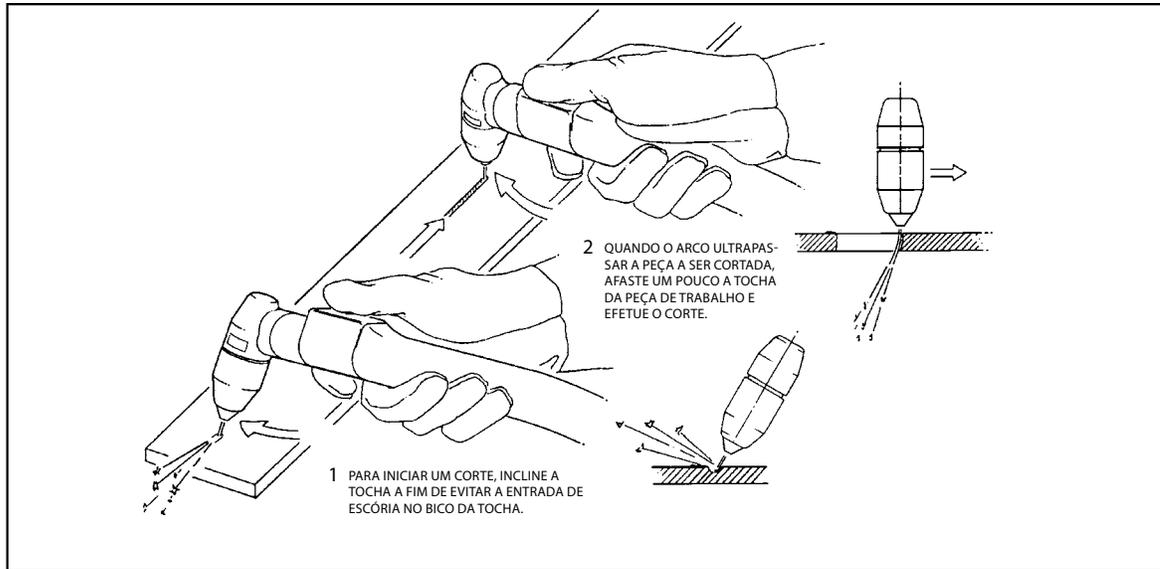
Técnica de furo utilizando a tocha PT-32EH.
